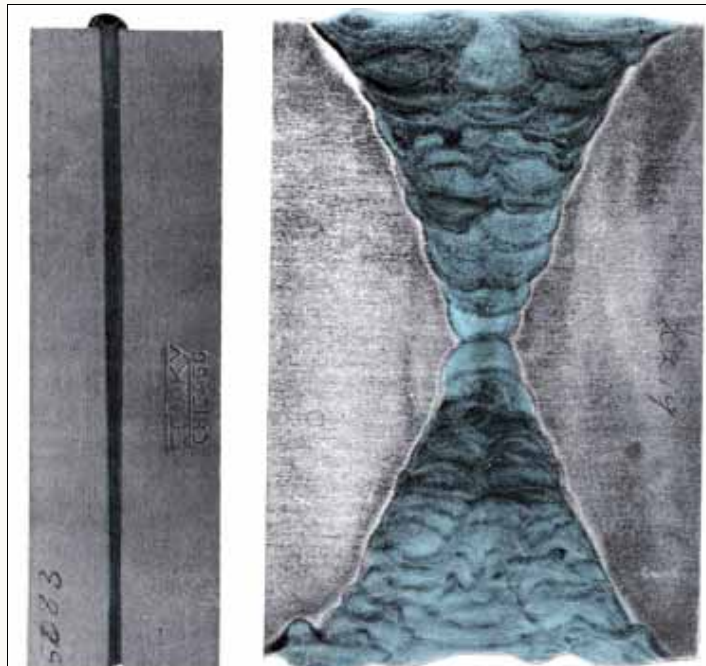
Alliage d'aluminium de 125 mm d'épaisseur. (a) soudure par faisceau d'électrons ayant un rapport H/L de 44/1, 54 kV, 0.5A, 1 passe, 40 cm/min (b) soudure MIG, 94 passes, 1cm/min
